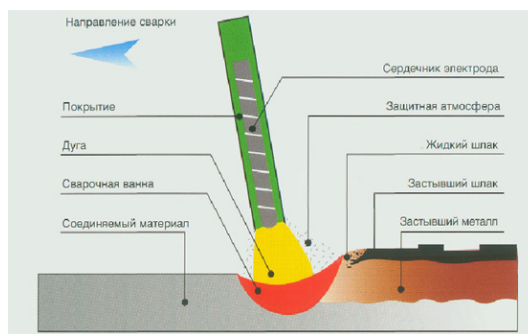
Схема ручной электродуговой сварки
